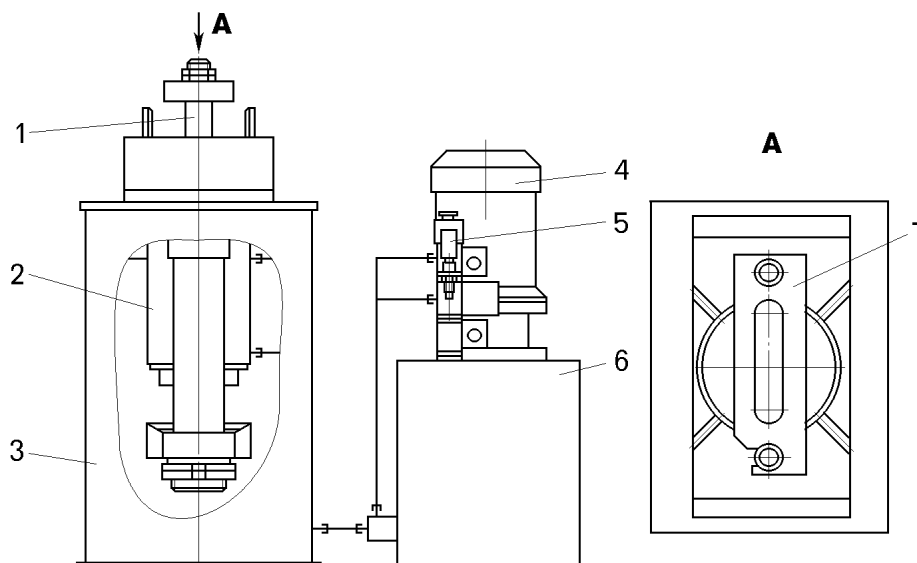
Установка для регулировки натяга манжеты:
